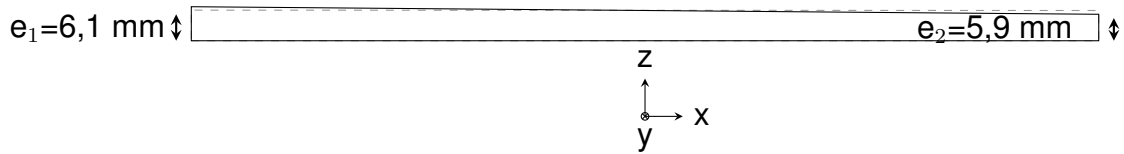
Section trapézoïdale dans le plan (xz)
